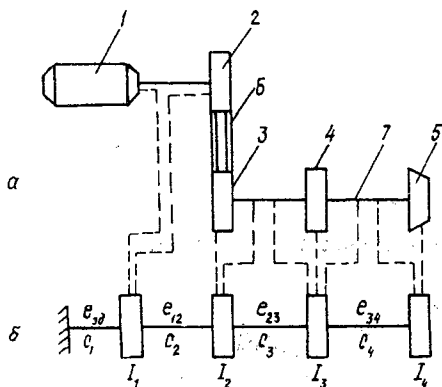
Кинематическая (а) и эквивалентная (б) схемы исследуемой системы фрезерного узла станка ФБС-750: 1 – электродвигатель; 2, 3 – шкивы клиноременной передачи ($r_3 = 30$ мм, $r_2 = 23$ мм); 4 – тормозной шкив; 5 – фреза; 6 – клиновые ремни; 7 – рабочий (приводной) вал фрезерного узла
